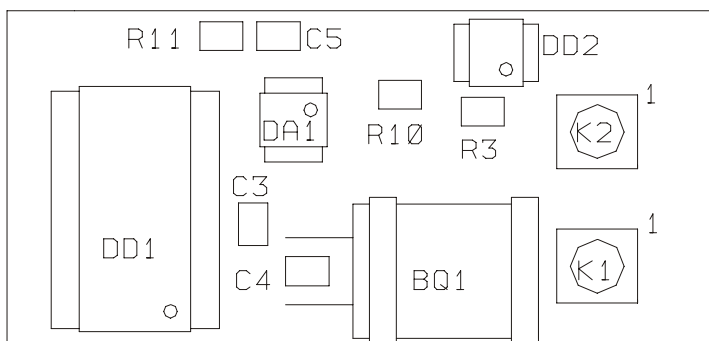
Сборочный чертеж платы обработки блока датчика СКГГ варианта исполнения 1. Сторона монтажа.
